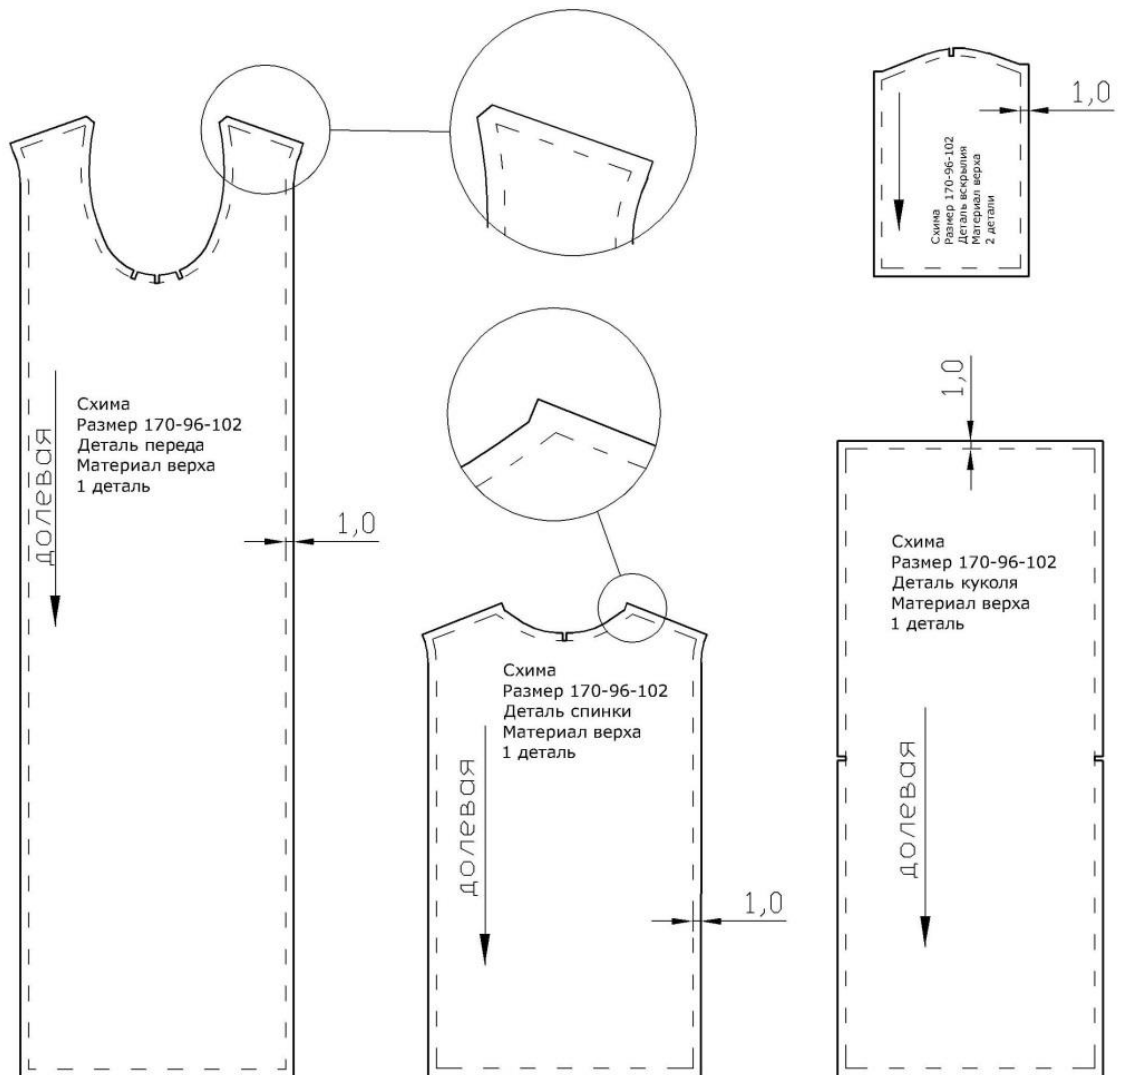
Лекала деталей схемы для раскроя материала верха с детализацией оформления уголков
